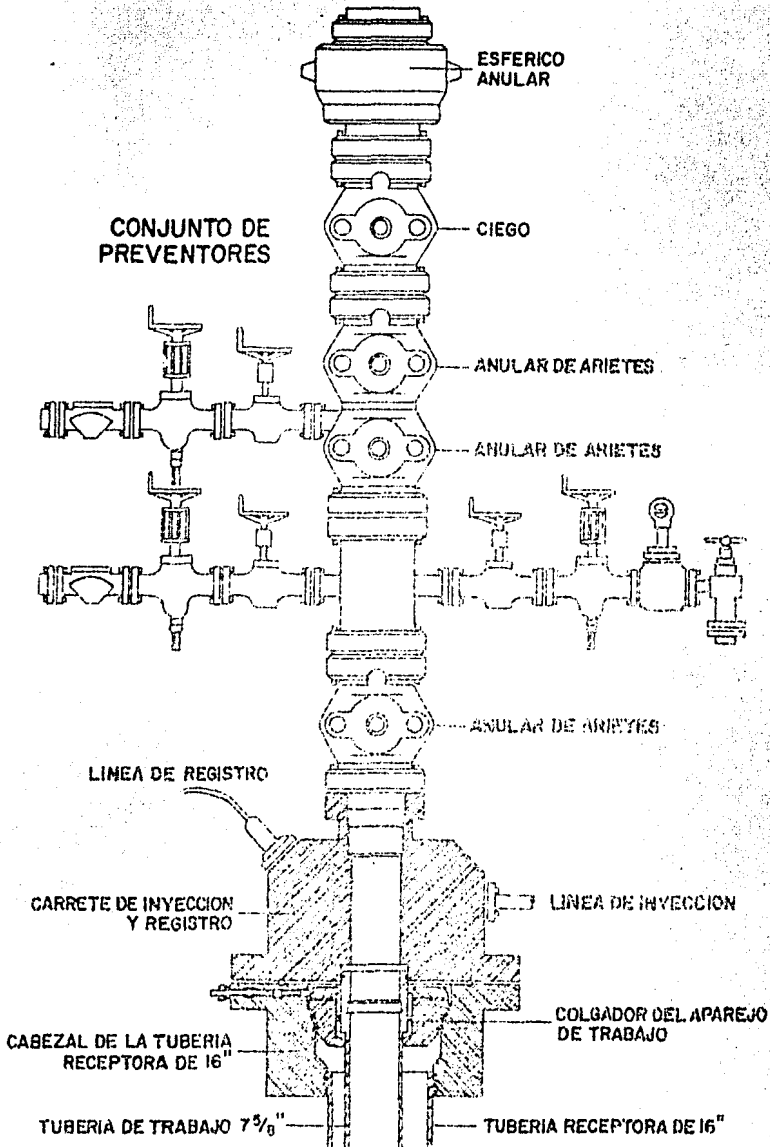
CONJUNTO DE PREVENTORES, CARRETE Y CABEZAL
